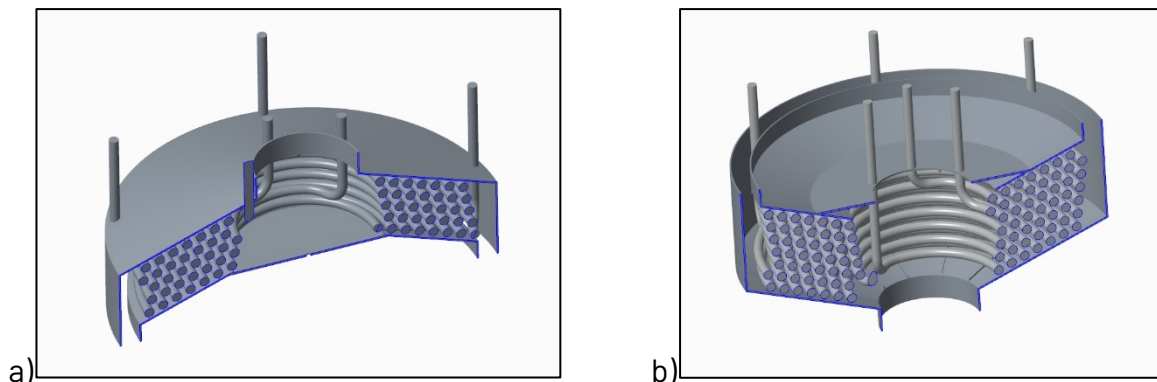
Design degli scambiatori di a) carica e di b) scarica
